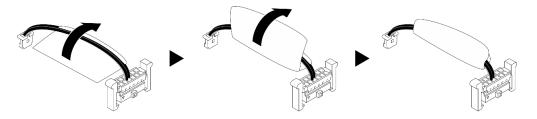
Rollen des Etiketts um das Kabel des COM-Ports
